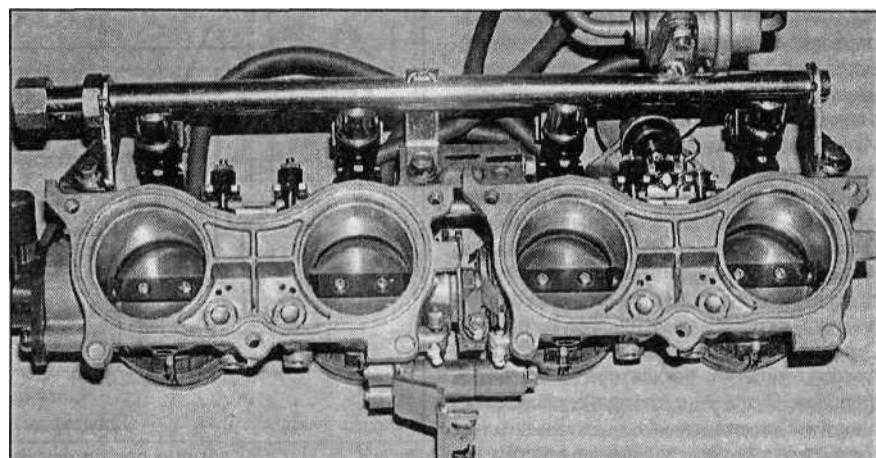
е Дроссельный патрубок в сборе с топливным коллектором (рампой) и форсунками (CBP.600F-1)
